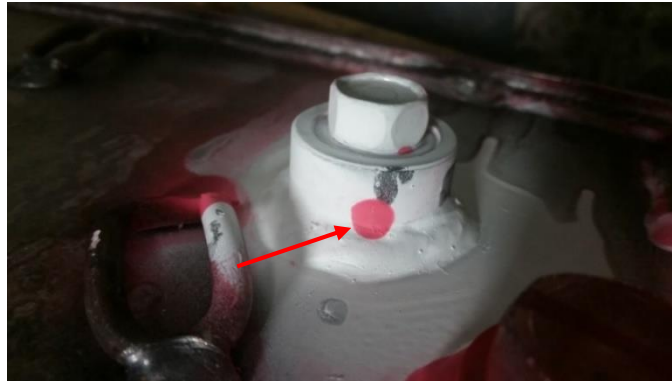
Defecto en componente revelado con líquidos penetrantes (30)
